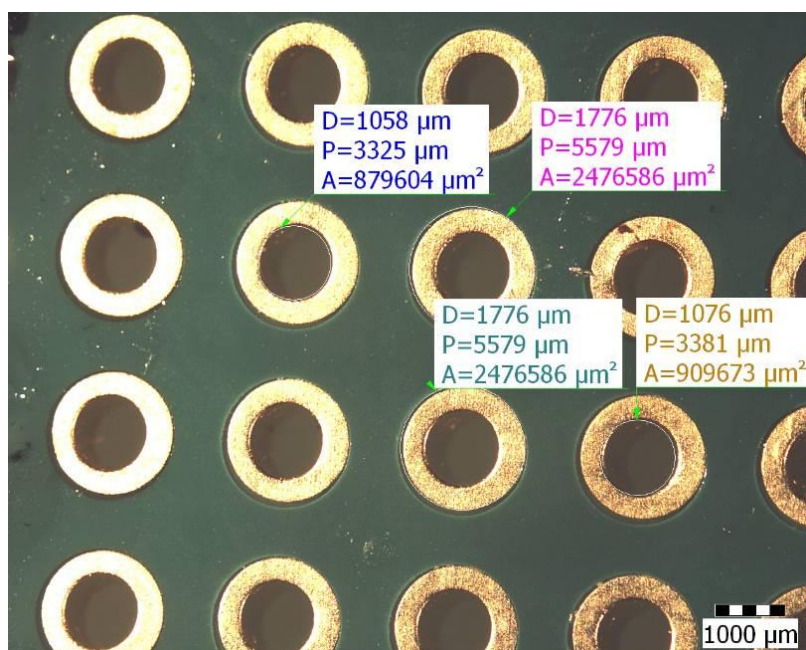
THT vývody tloušťky 0,7 mm před měřením
